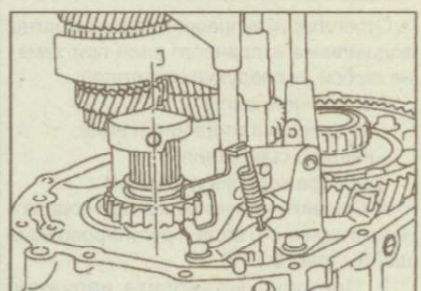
Совмещение отверстия шестерни 4-й передачи и установка промежуточной шестерни и вала передачи заднего хода
